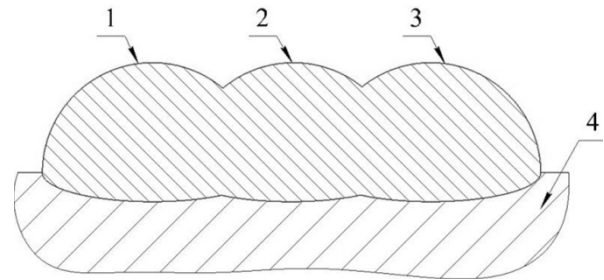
Схема наплавлених валиків: 1, 2, 3 — порядок наплавлення валиків; 4 — сталевий зразок з сталі Ст. 3
